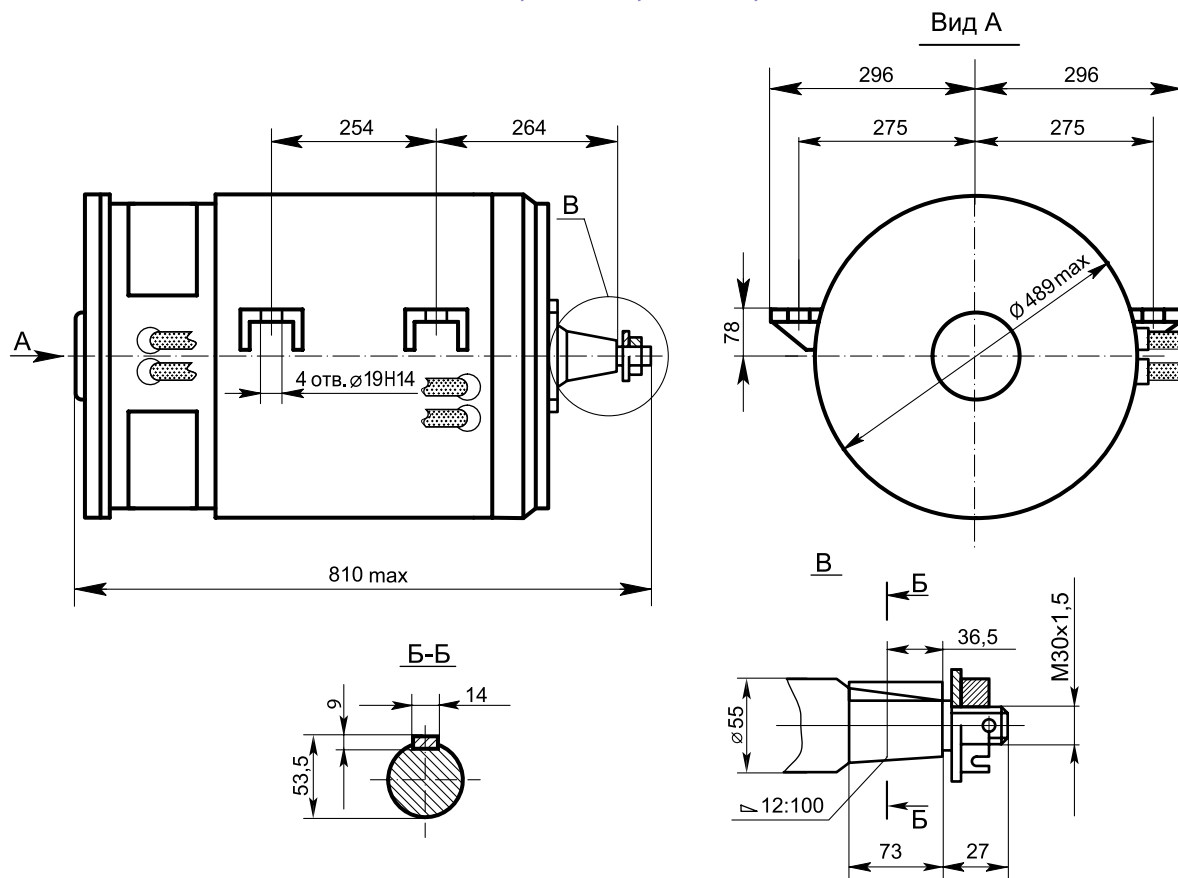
Габаритные, установочные, присоединительные размеры электродвигателей ДК-309М
